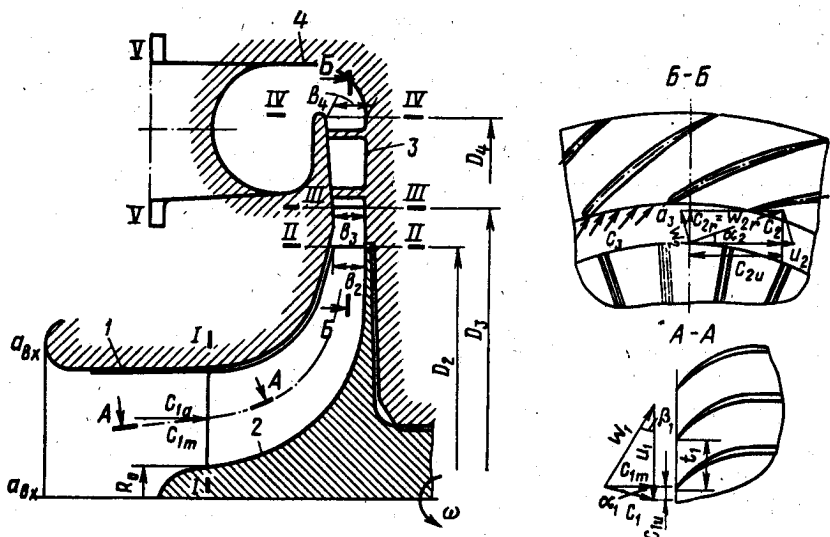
Схема проточной части центробежного компрессора с лопаточным диффузором:
